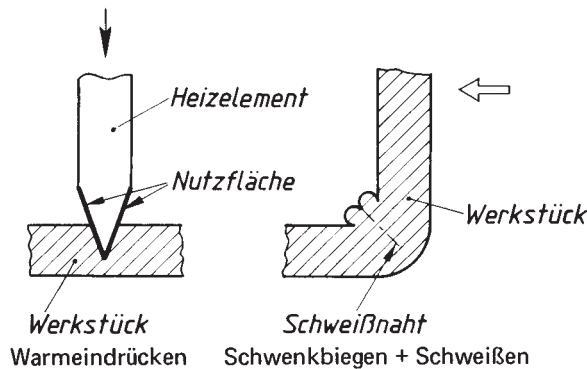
Heizelement-Schwenkbiegeschweißen
